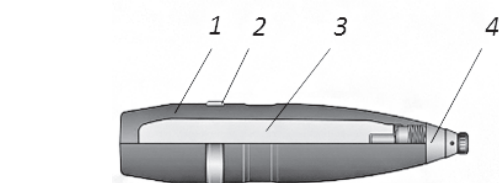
Конструкция ОФС: 1 — корпус; 2 — ведущий пояс; 3 — разрывной заряд; 4 — взрыватель
